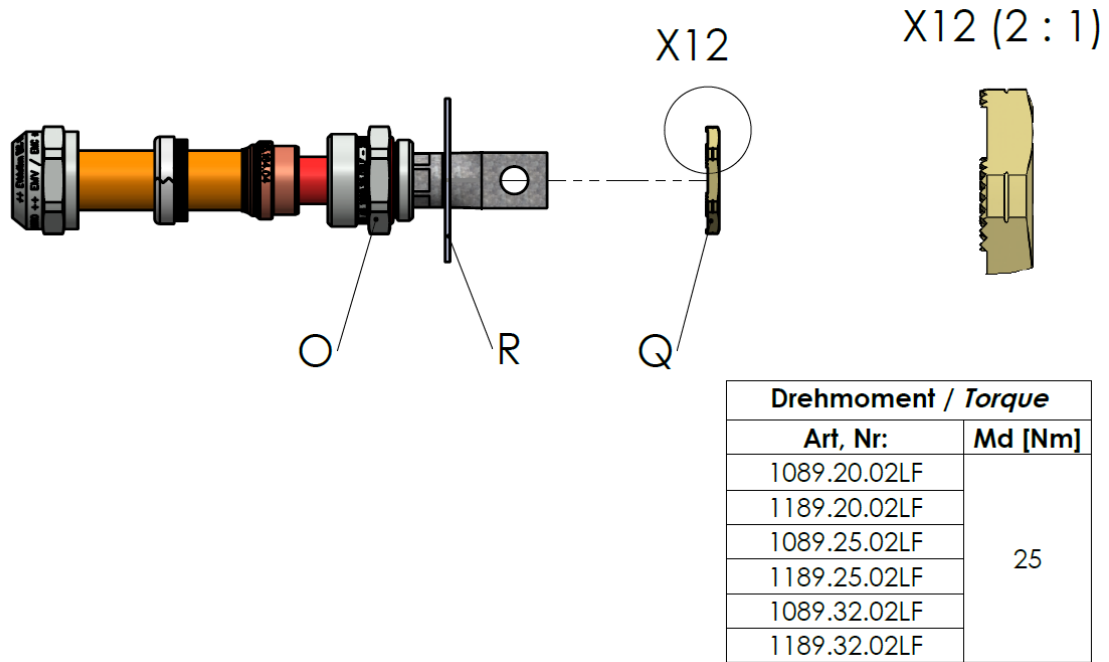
Montaggio del manicotto di connessione su lamiera con controdado
